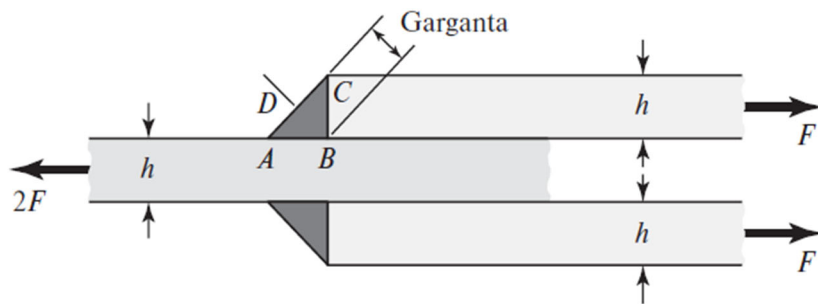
Soldadura con filetes transversales. [24]
